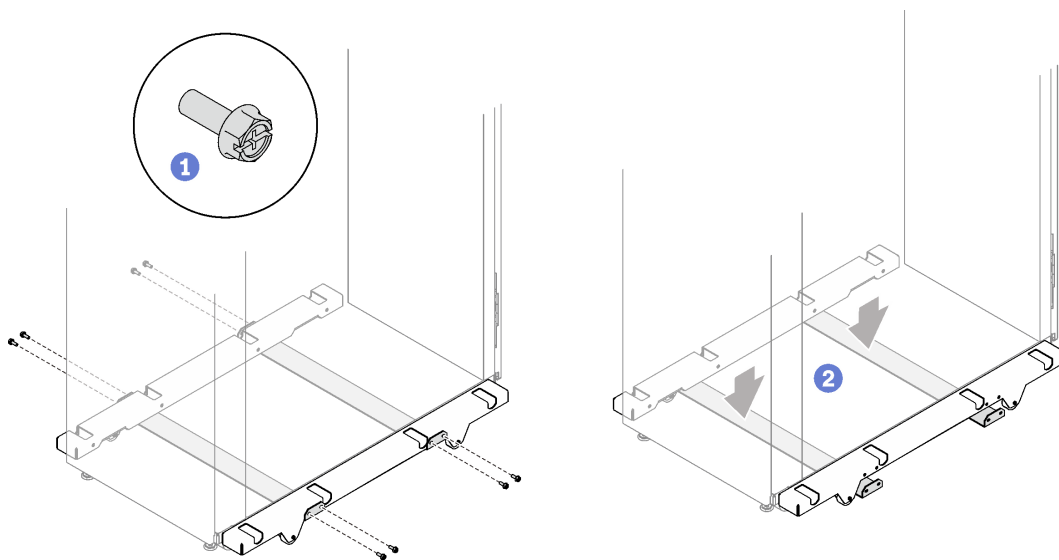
Extracción de las barras estabilizadoras de los estabilizadores
